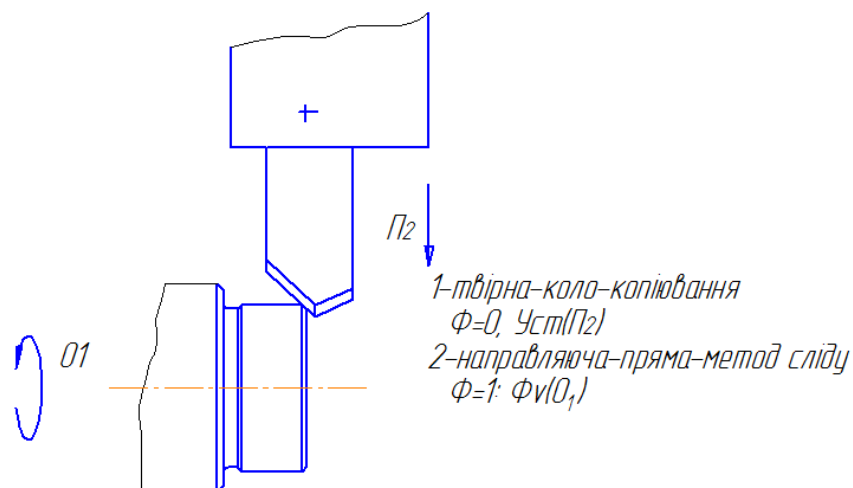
Комплекс формоутворюючих рухів при обертovому русі заготовки та поступальному руху різця
